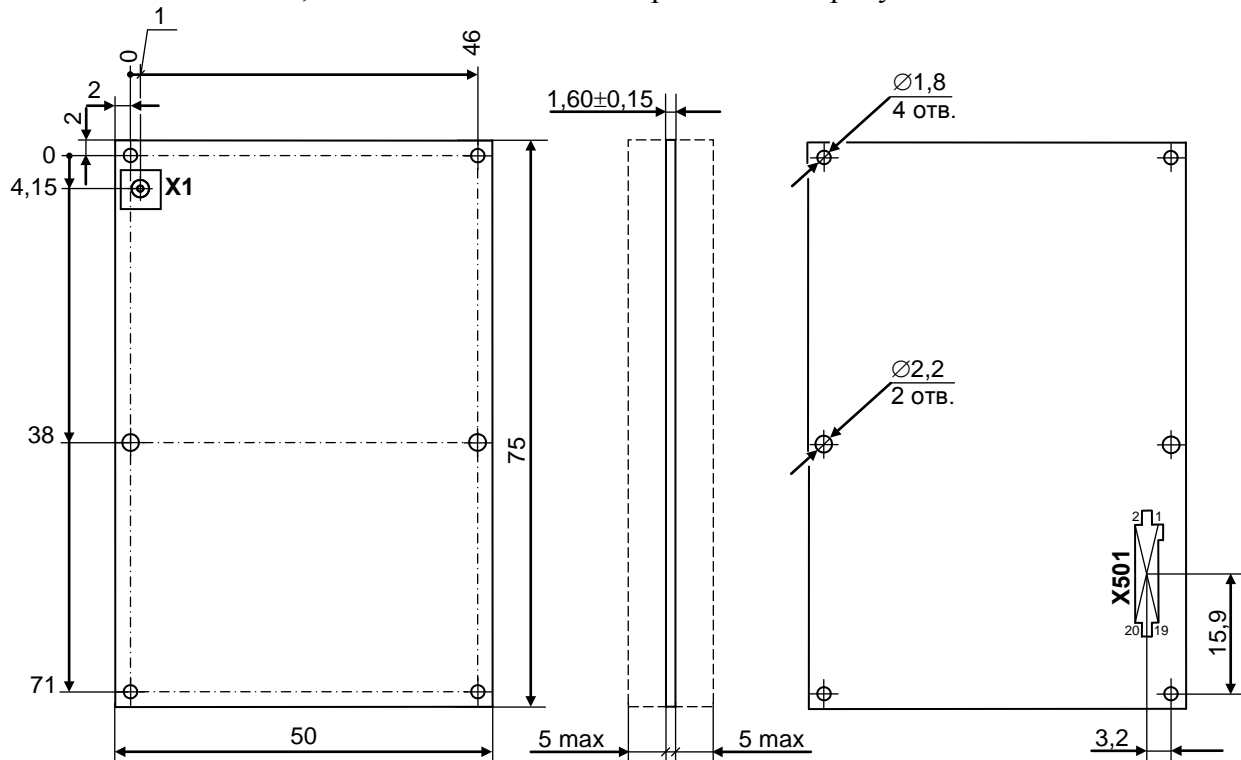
Габаритные и установочные размеры ПН АПМА.468173.002-01
